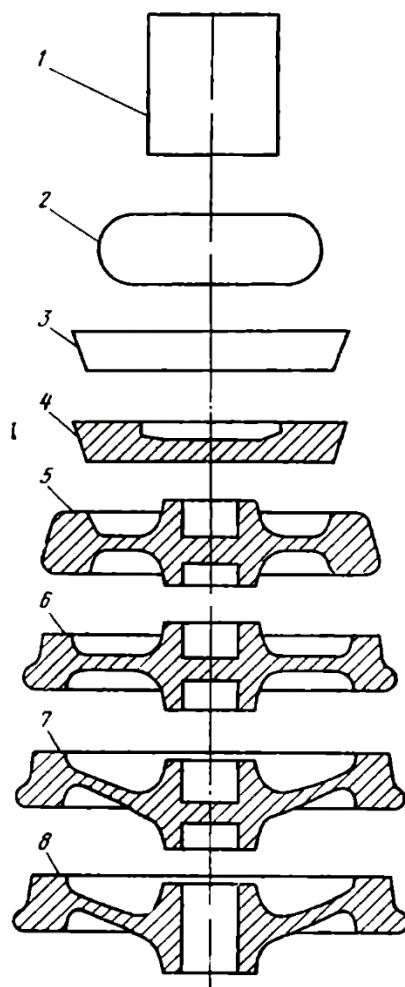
Схема формоизменения заготовки при производстве цельнокатаного железнодорожного колеса на прессопрокатных линиях ПАО «Интерпайп НТЗ» и АО «ВМЗ»: 1 – заготовка; 2 – заготовка после свободной осадки; 3 – заготовка после осадки в кольце; 4 – заготовка после разгонки; 5 – заготовка после штамповки; 6 – заготовка после прокатки; 7 – заготовка после выгибки диска и калибровки; 8 – заготовка после прошивки отверстия [3]
